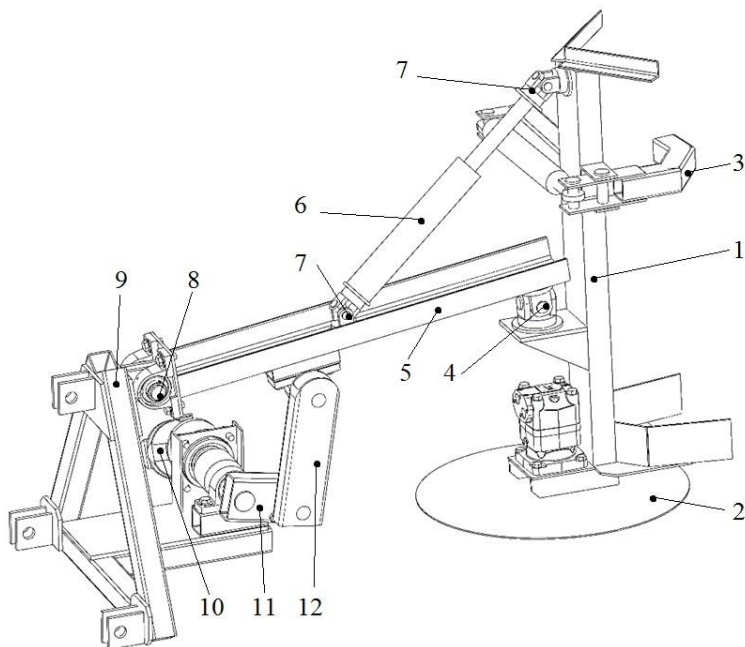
Общий вид захватно-срезающего устройства с виброприводом:
